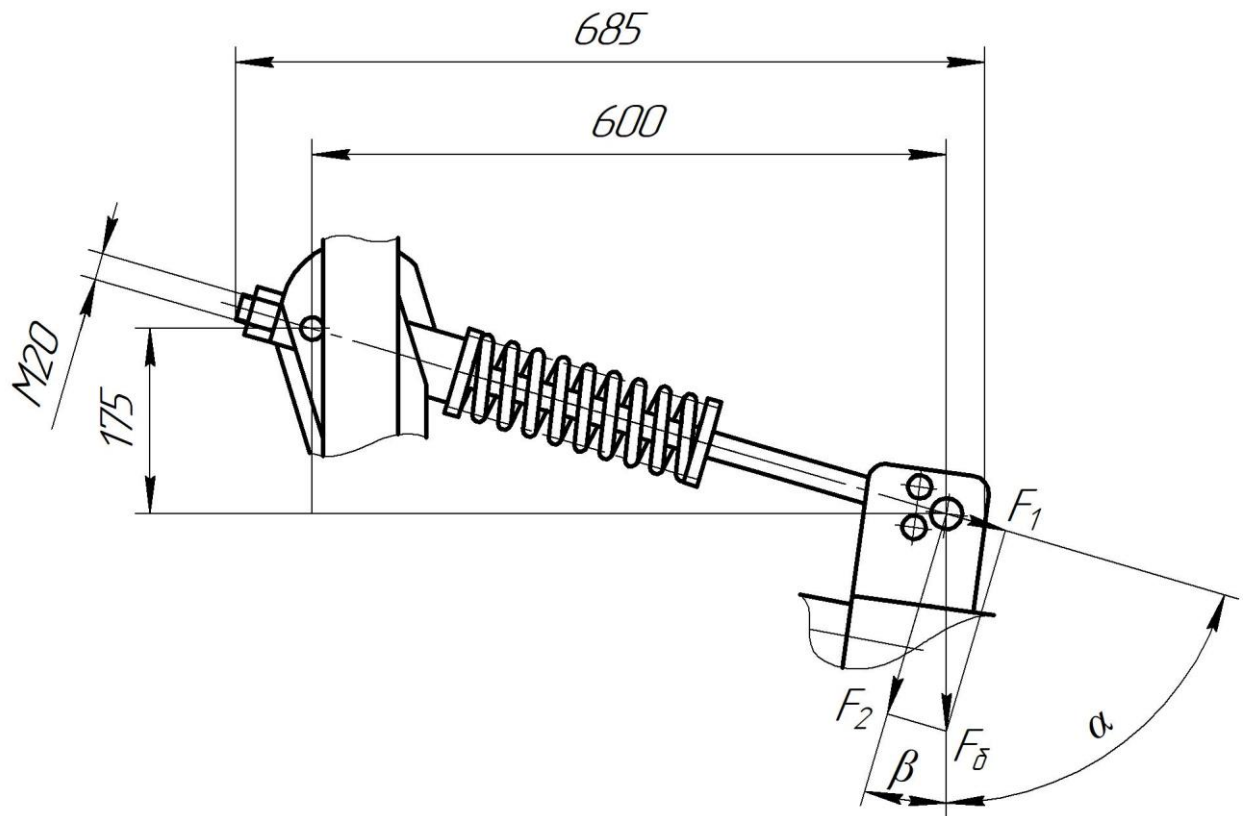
Схема для визначення зусиль різьбового з'єднання
